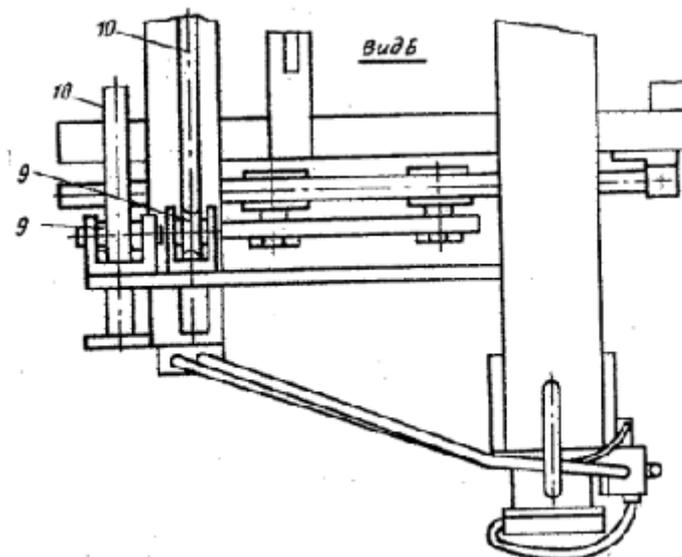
Вид Б станда для разборки и сборки коробок передач
